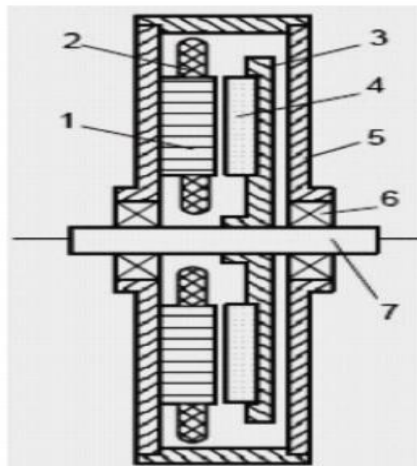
Descriptif de la machine à flux axial 1 stator / 1 rotor.
